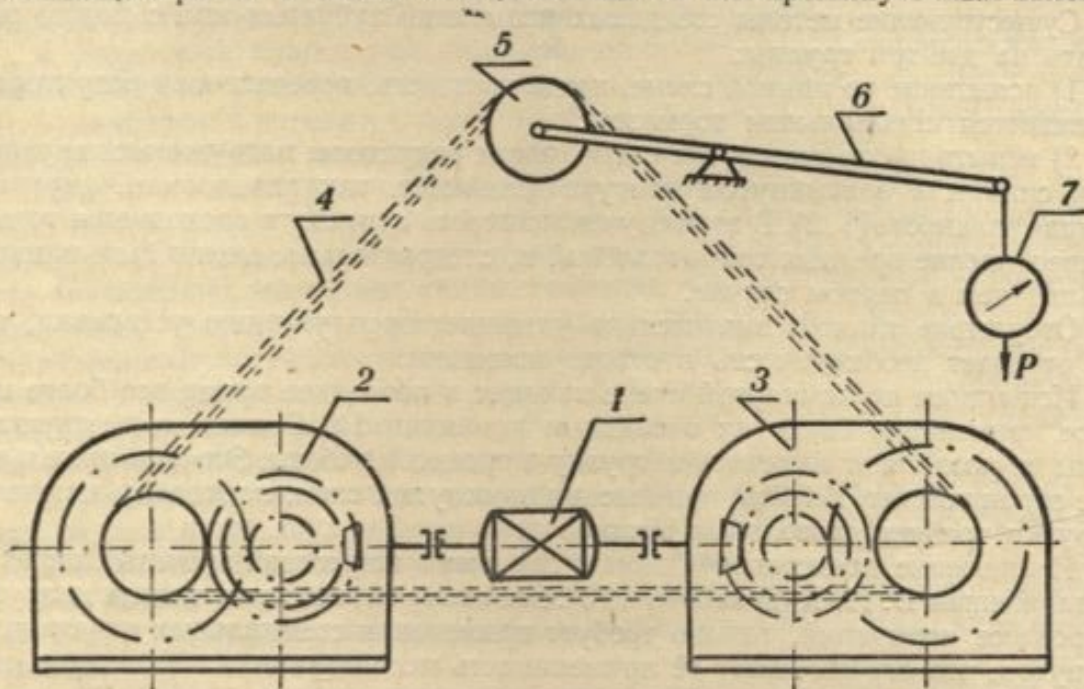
1 — Электродвигатель, 2, 3 — испытуемые редукторы, 4 — втулочно-роликовая цепь, 5 — звёздочка, 6 — рычаг, 7 — динамометр.
